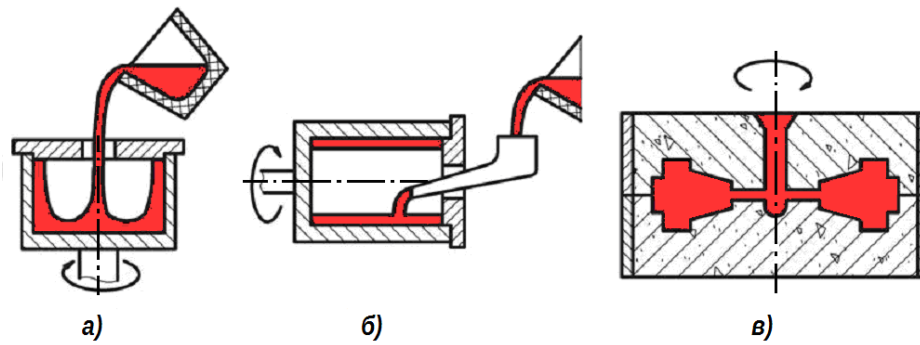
Схеми роботи устаткування для відцентрового лиття:
